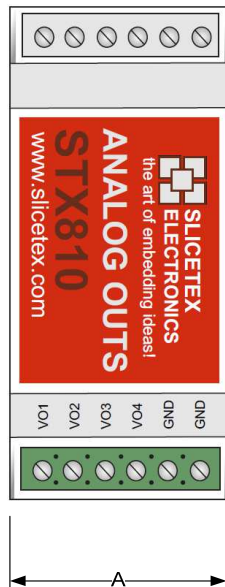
Dimensiones vista superior – Versión STX810-BOARD
